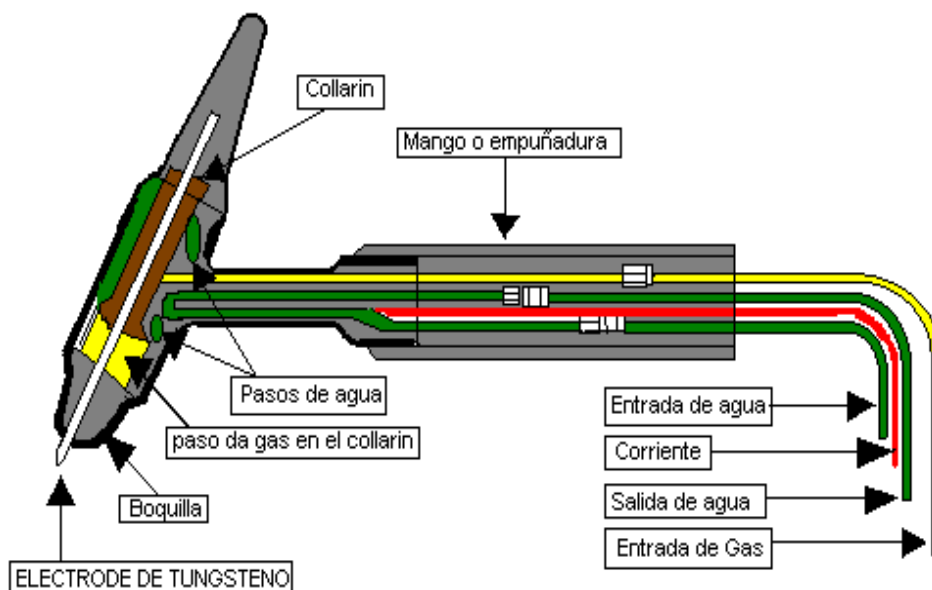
Torcha o pistola de soldadura GTAW
